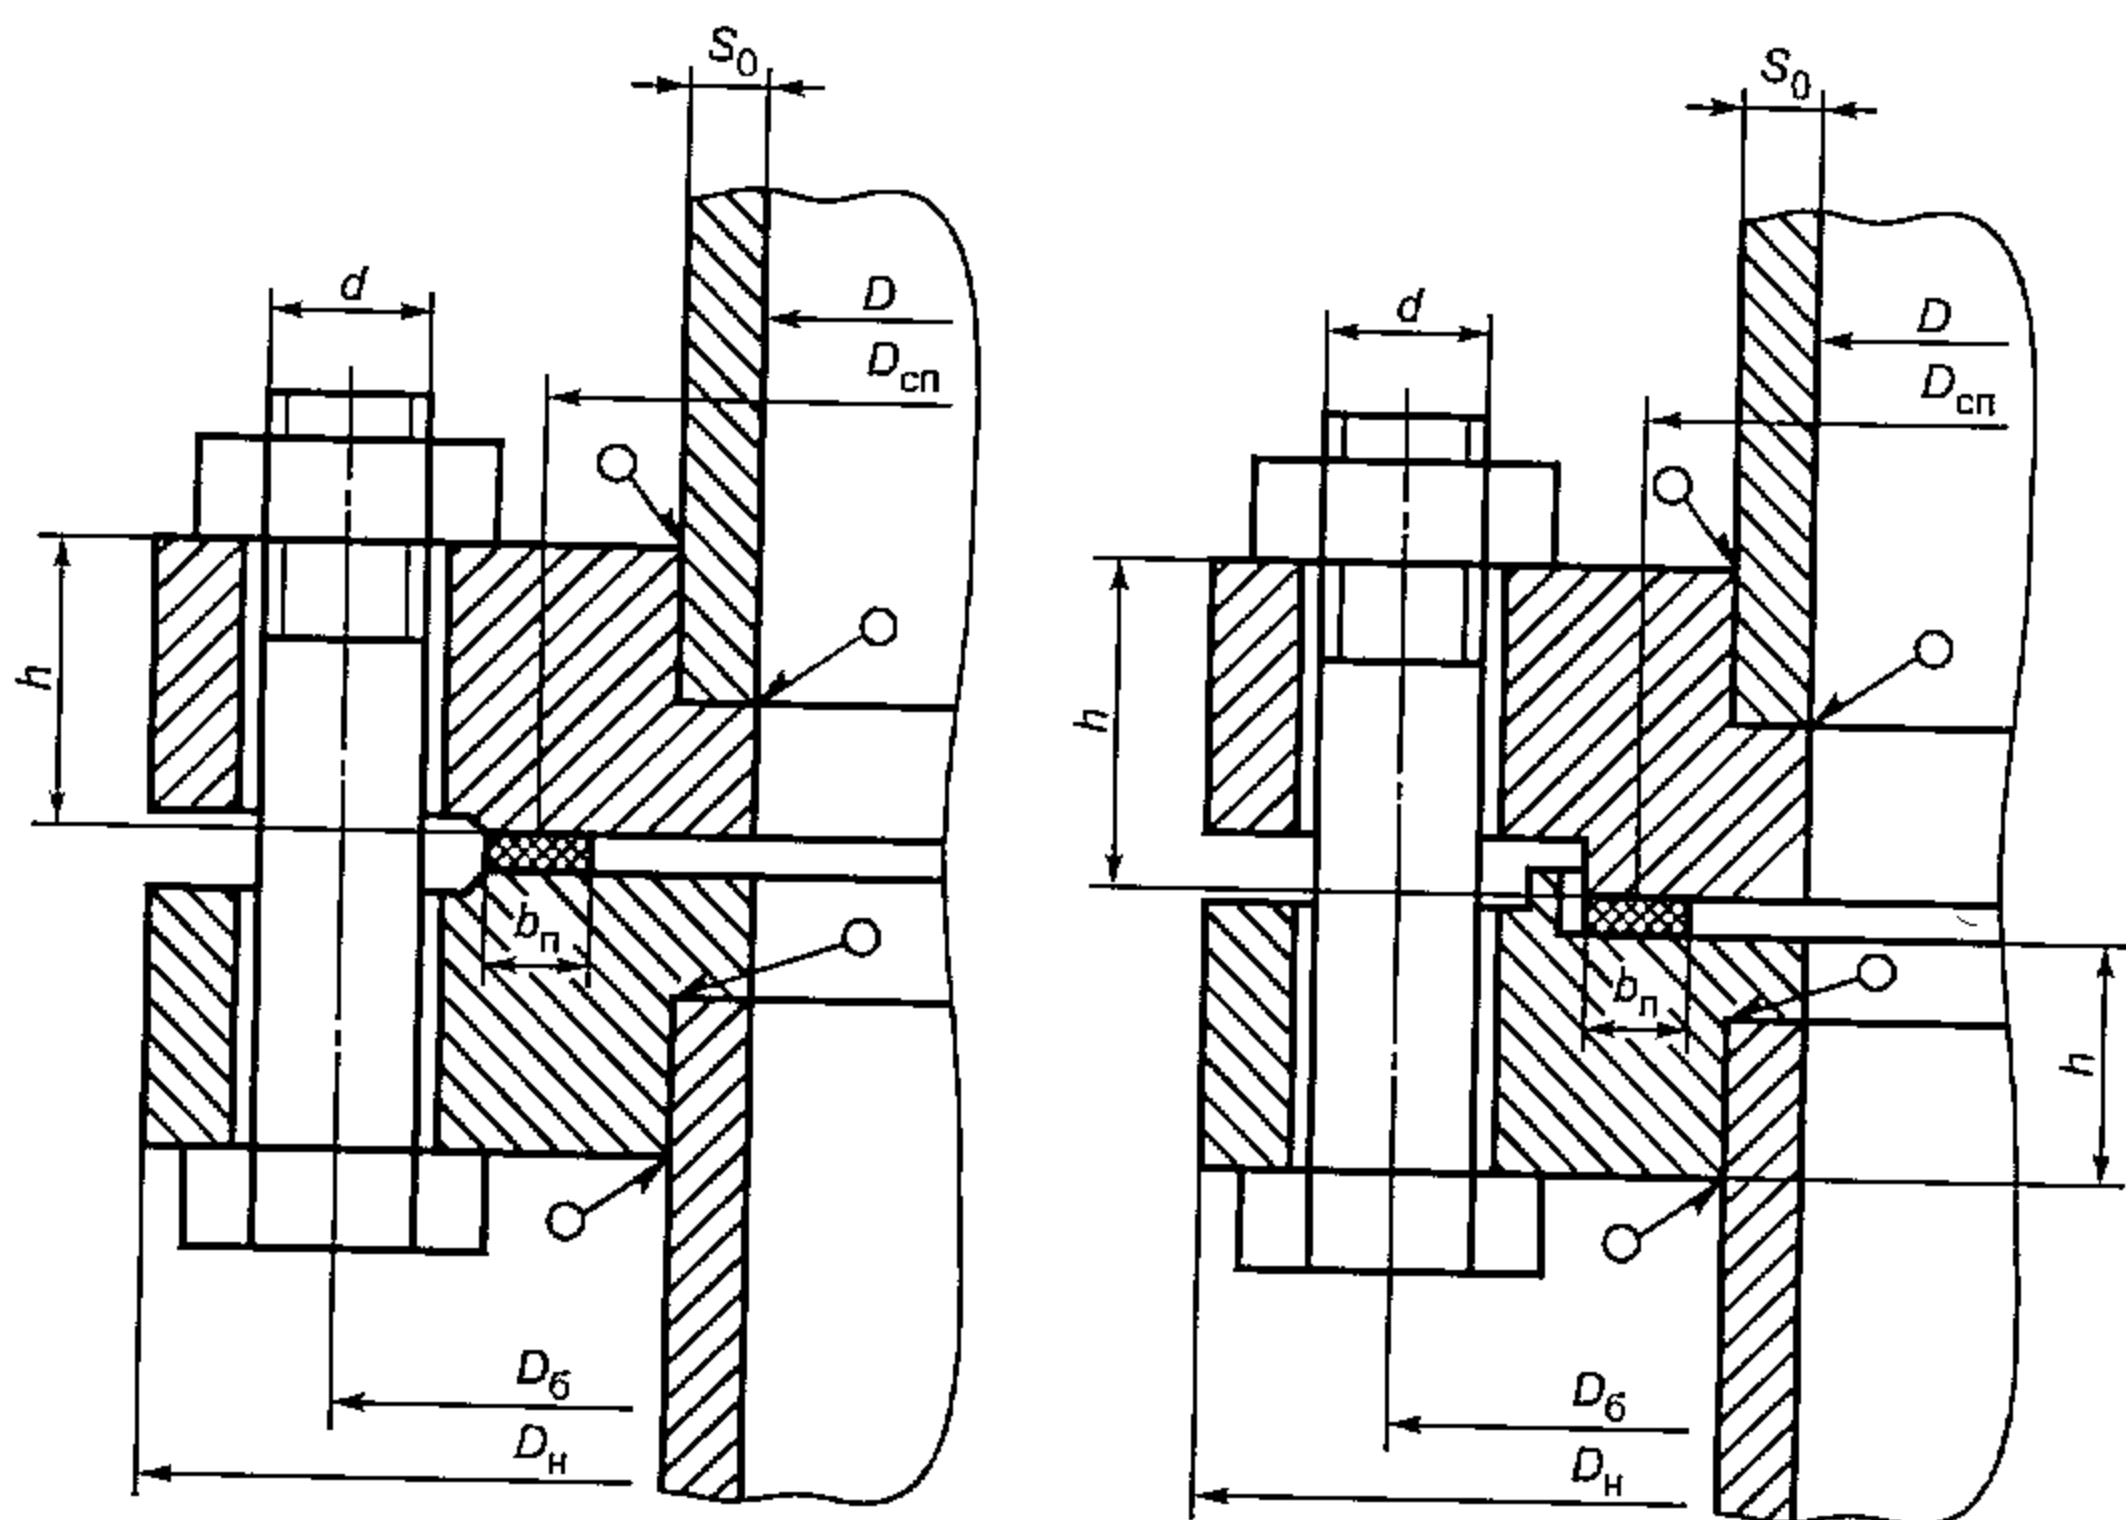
, лист 1 — Фланцевые соединения с приварными встык фланцами
